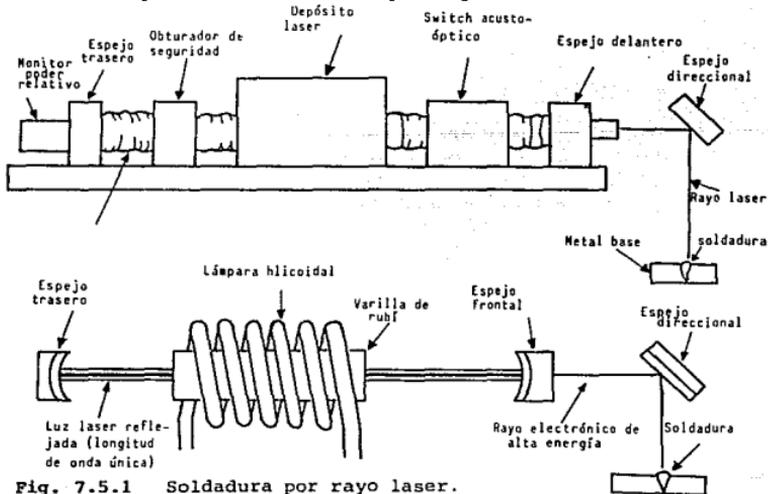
Soldadura por rayo laser.
